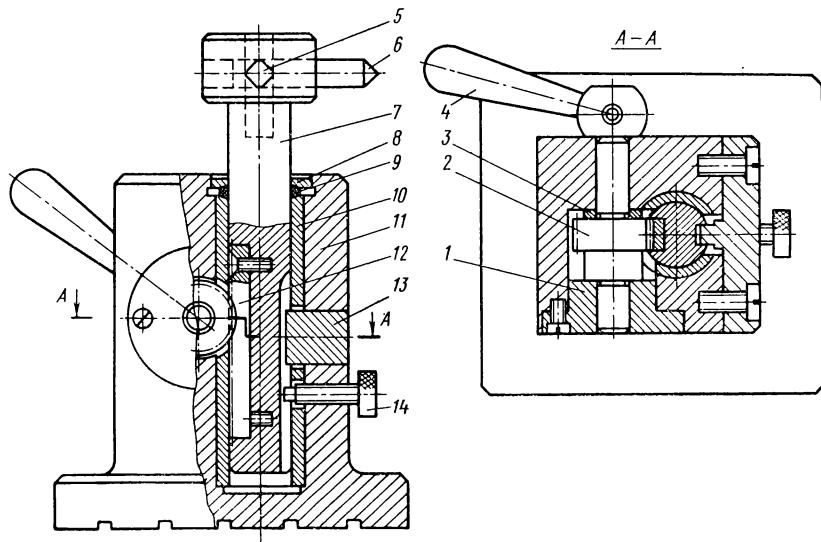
Приспособление для профилирования шлифовального круга на поворотной магнитной плите
